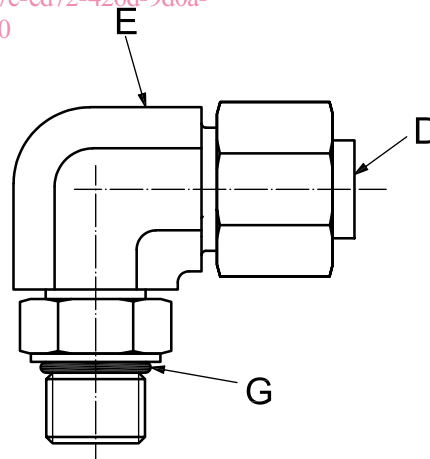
Montage d'essai pour raccordement de tube — Type 1
